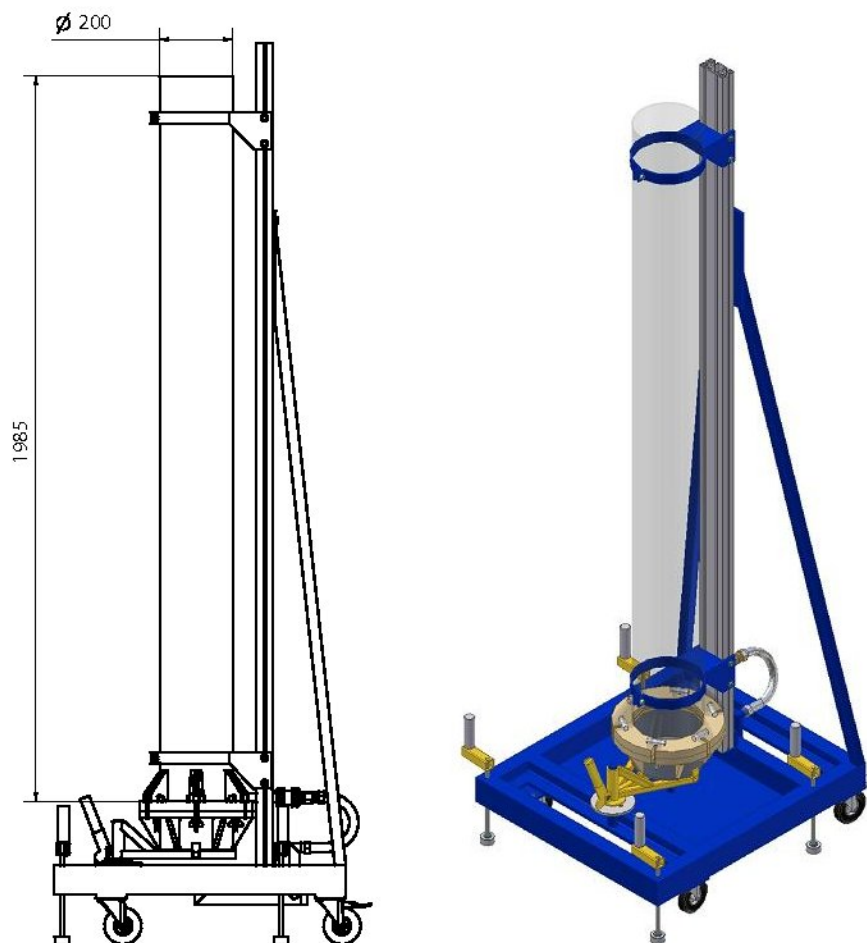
Plan du tube de sédimentation (dessin : S. Haquin) et vue 3D. Les dimensions sont exprimées en millimètres.
